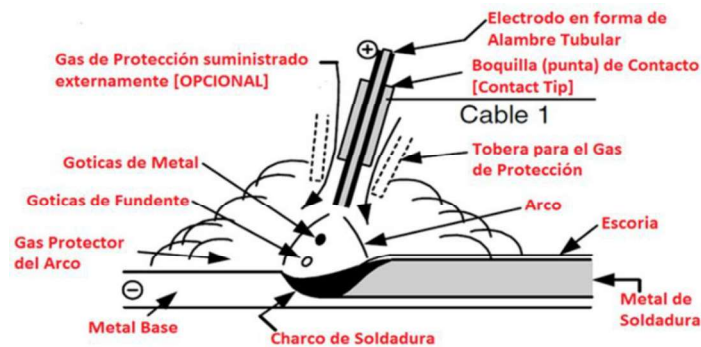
Esquema detallado del arco del proceso de soldadura FCAW.
